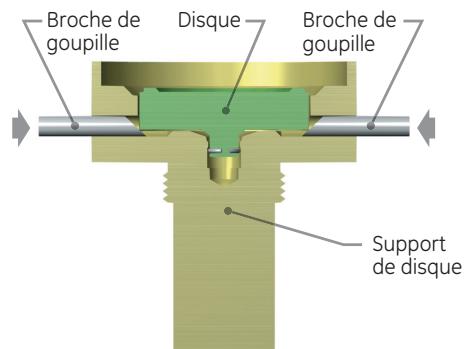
Désinstaller le disque avec des anneaux d'assemblage
